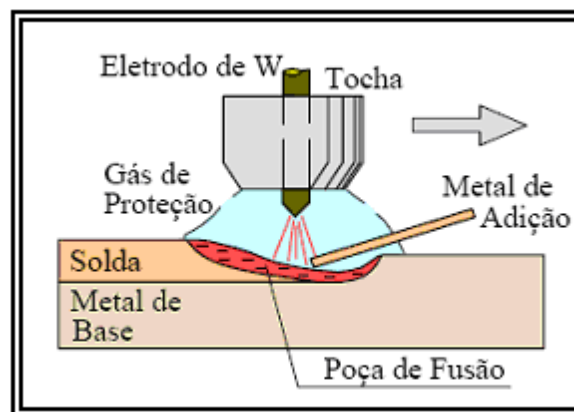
Soldagem TIG (Esquemática) (Marques, 2007).
